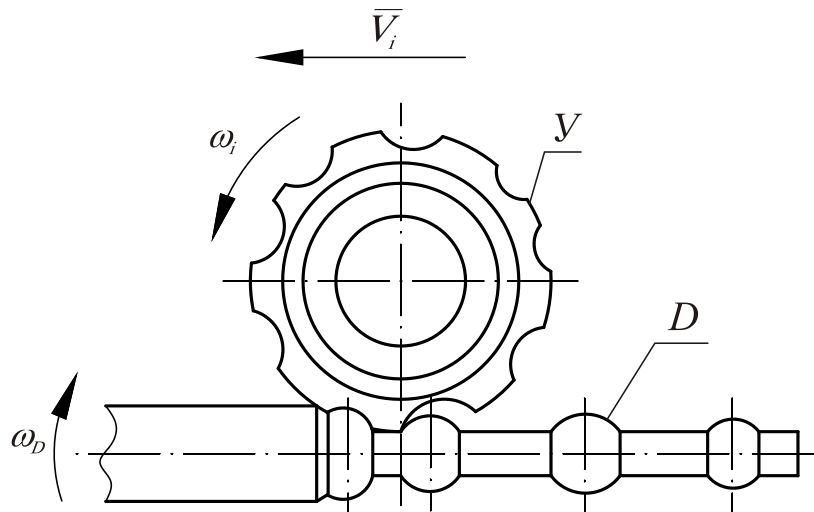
Оброблення поверхні обертання чашковим різцем
